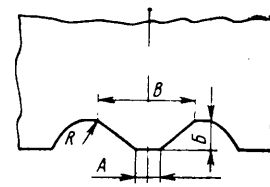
Выступ, выполненный заподлицо с торцом заготовки
